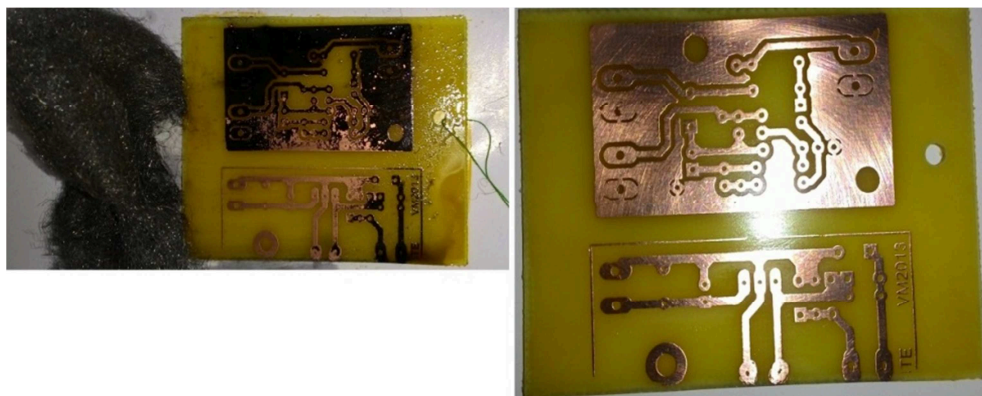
Desenho do circuito com ajustes à mão.
